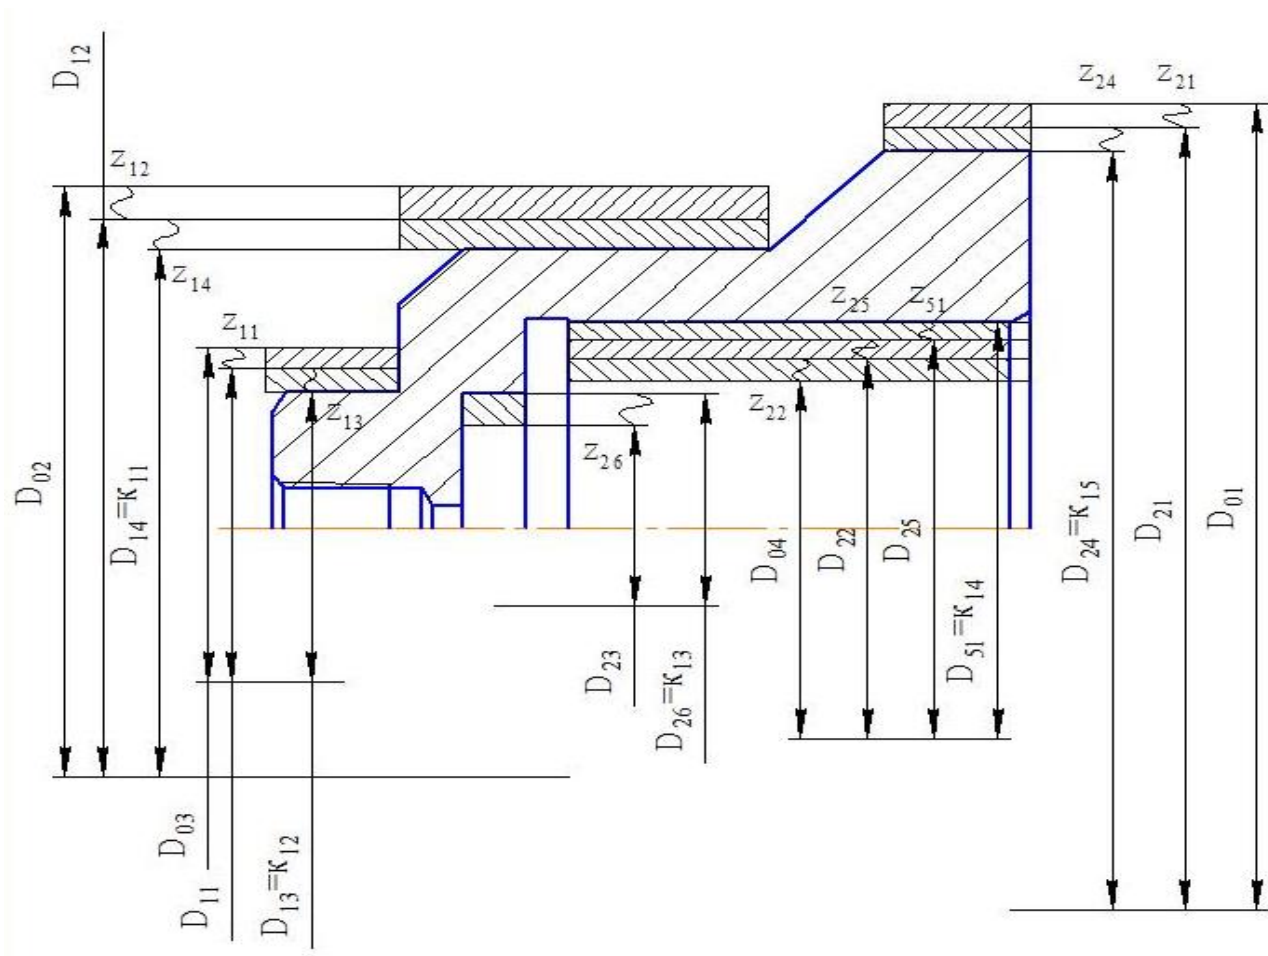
Размерная схема технологического процесса изготовления детали «Корпус» (диаметральное направление).
